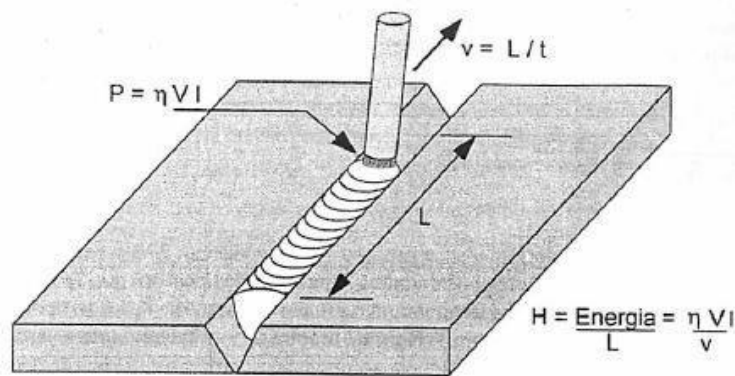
Esquema explicativo do aporte térmico da soldagem (Adaptado de [5]).
